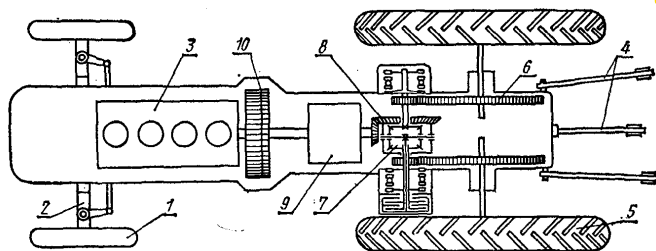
Схема розміщення основних частин, їх механізмів і деталей колісного трактора МТЗ-80: 1 – керуюче колесо; 2 – передній міст; 3 – двигун; 4 – механізм навіски; 5 – ведуче колесо; 6 – кінцева передача; 7 – диференціал; 8 – головна передача; 9 – коробка передач; 10 – зчеплення
